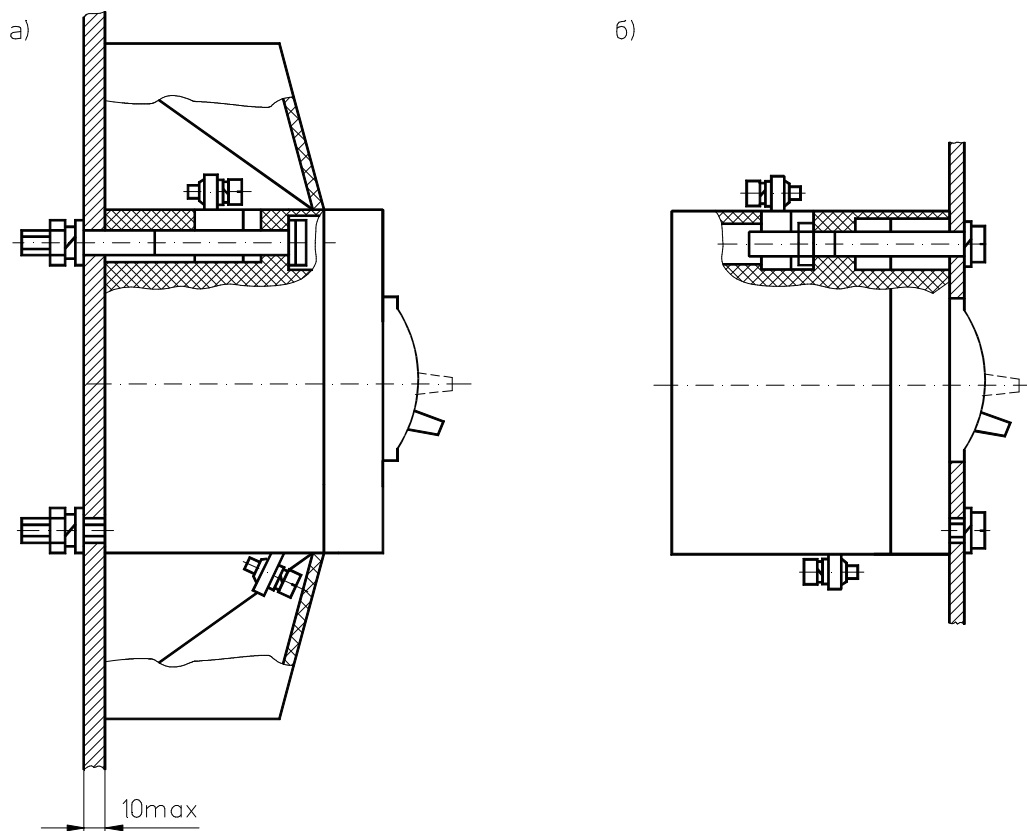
Крепление выключателя в пластмассовой оболочке
